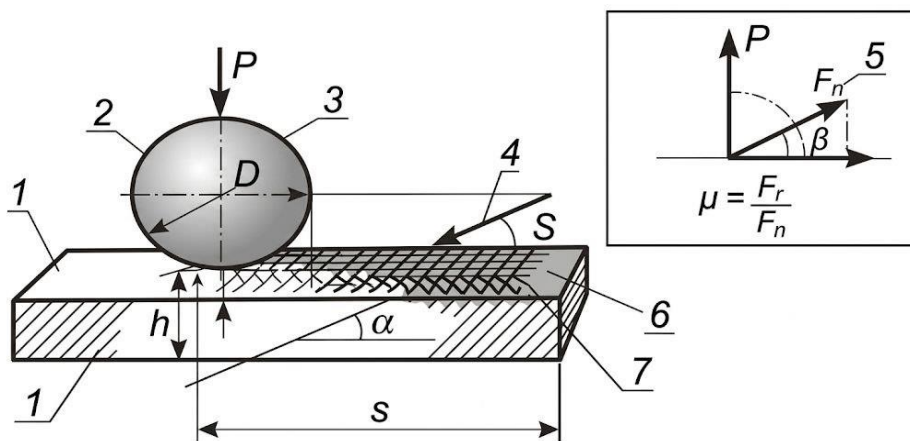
Схема формирования регулярного узора на плоской детали: 1- плоская деталь (лист или пластина); 2 - стальной шариковый инструмент; 3 - направление перемещения инструмента; 4 - подача S ; 5 - усилие прижатия P ; 6 - зона пластической деформации; 7 - элементы регулярного узора.
